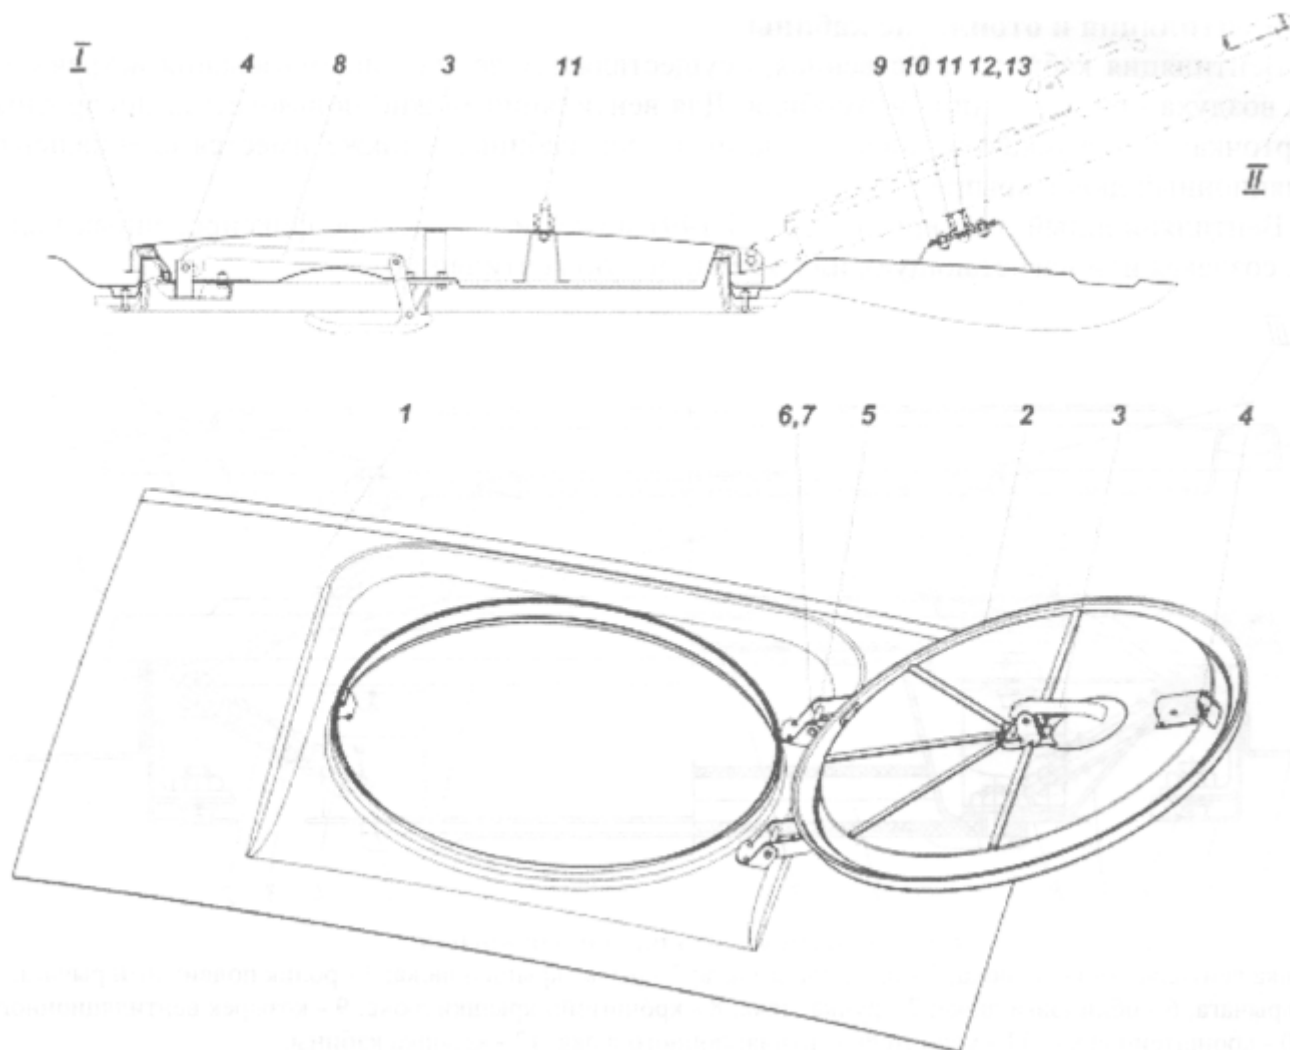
Люк вентиляционный крыши: 1 - крышка вентиляционного люка; 2 - пружина рычага; 3 - рычаг крышки люка; 4 - ролик подвижный рычага; 5 - упор рычага; 6 - облицовка люка; 7 - ручка люка; 8 - кронштейн крышки люка; 9 - козырек вентиляционного люка; 10 - кронштейн люка; 11 - усилитель вентиляционного люка; 12 - крышка кабины. I - закрытое положение крышки люка; II, III, IV - три открытых положения крышки люка.
